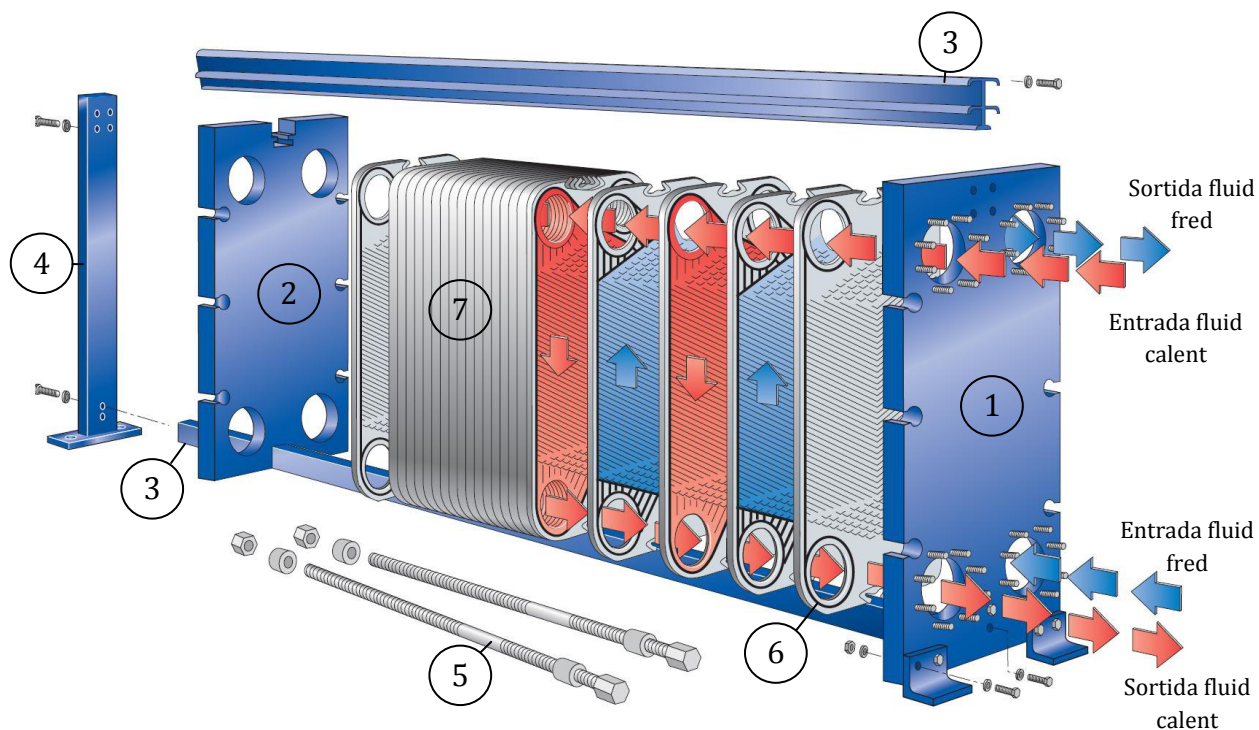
PARTS CONSTRUCTIVES D'UN BESCANVIADOR DE PLAQUES
